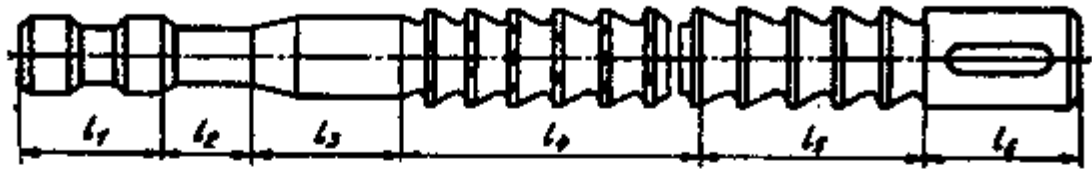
Ескізи інструментів: протяжка зі сталі Р6М5
